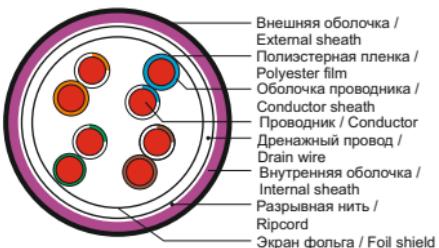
Конструкция кабеля типа F/UTP (с двойной оболочкой) / Figure 10 – Cable design of F/UTP type (double sheathed)
